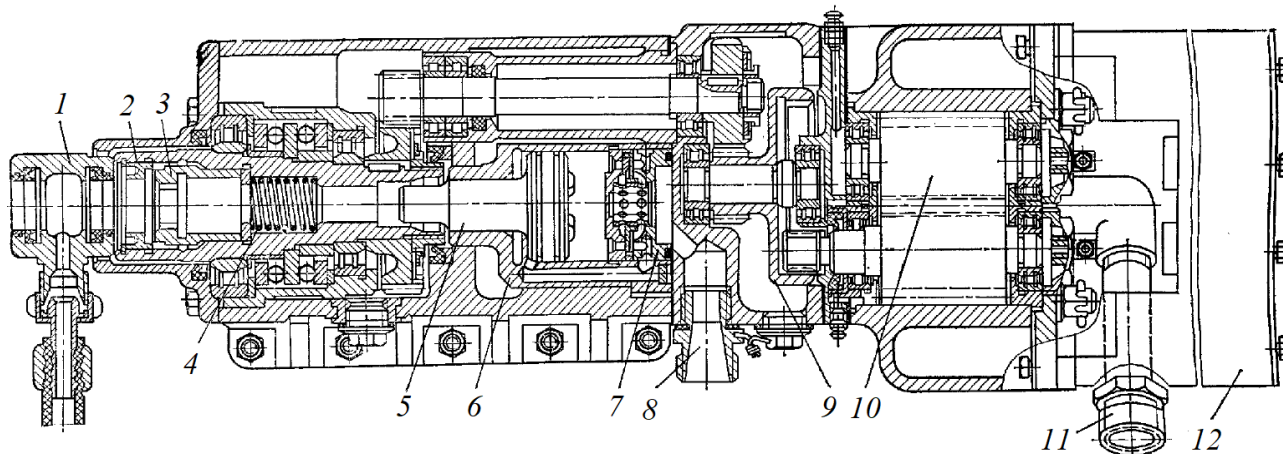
Бурова обертово-ударна головка 1100-1-1М:
